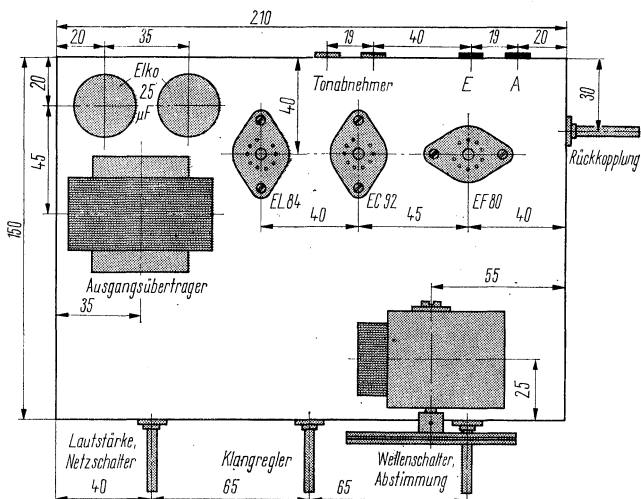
Aufbauplan eines einfachen Einkreisempfängers
